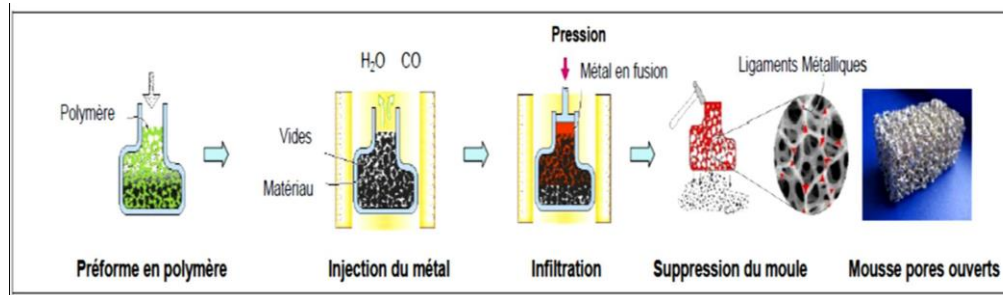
Procédé de fabrication des mousses d'aluminium par écoulement d'infiltration [48].
